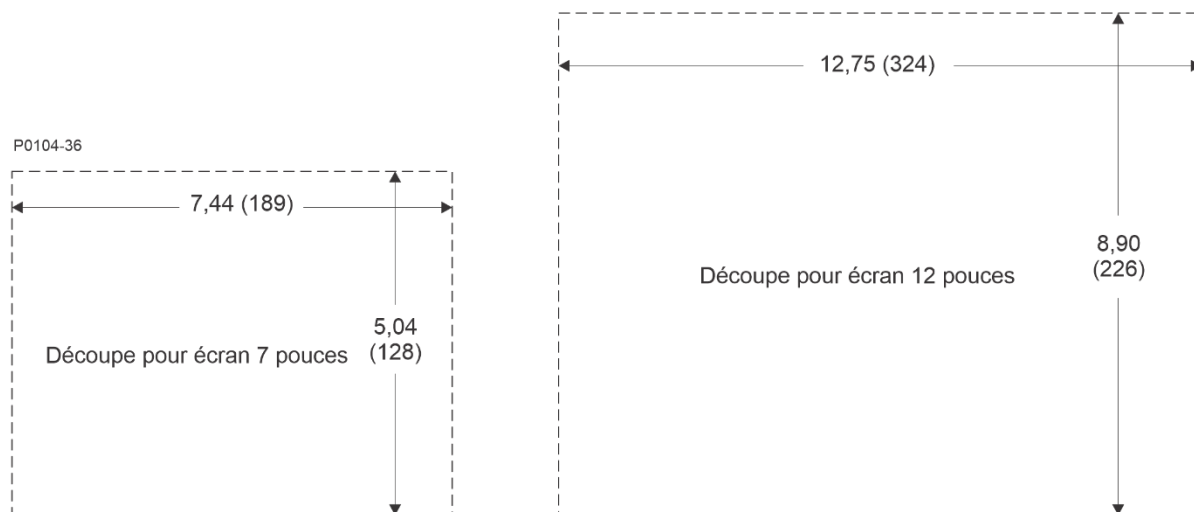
Dimensions de découpe du panneau de l'IDP-2020
